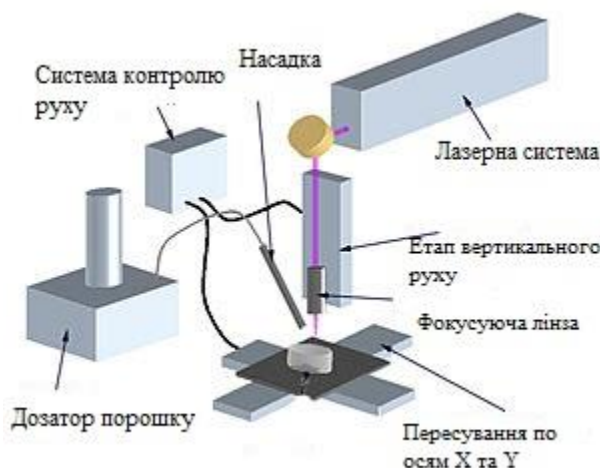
Схема установки для лазерного наплавлення [33]
